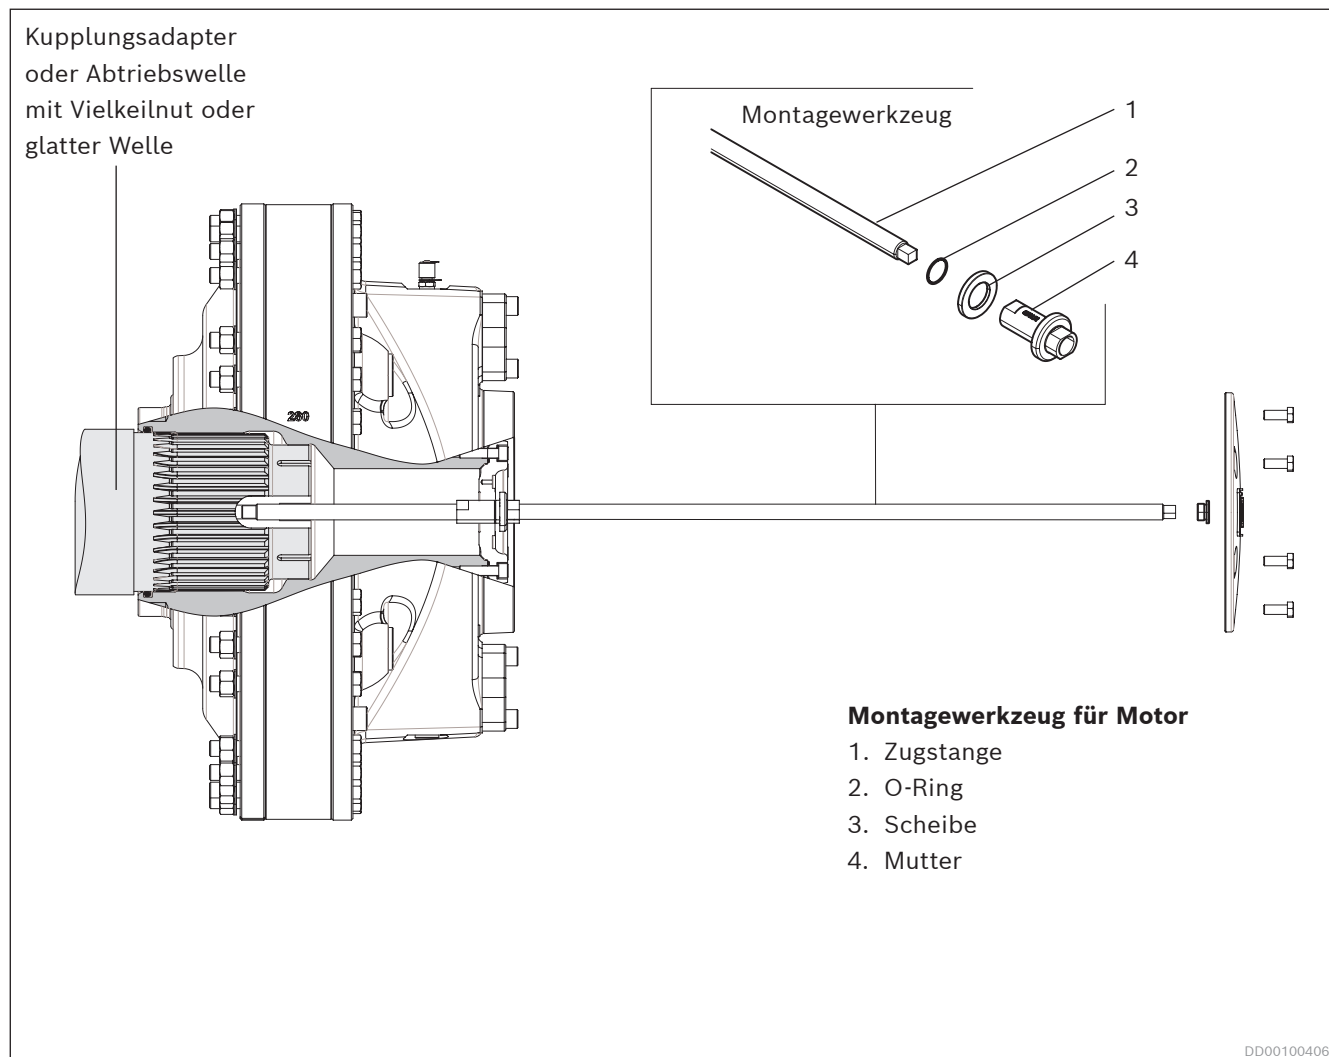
Montage von CB-Motor mit Montagewerkzeug
